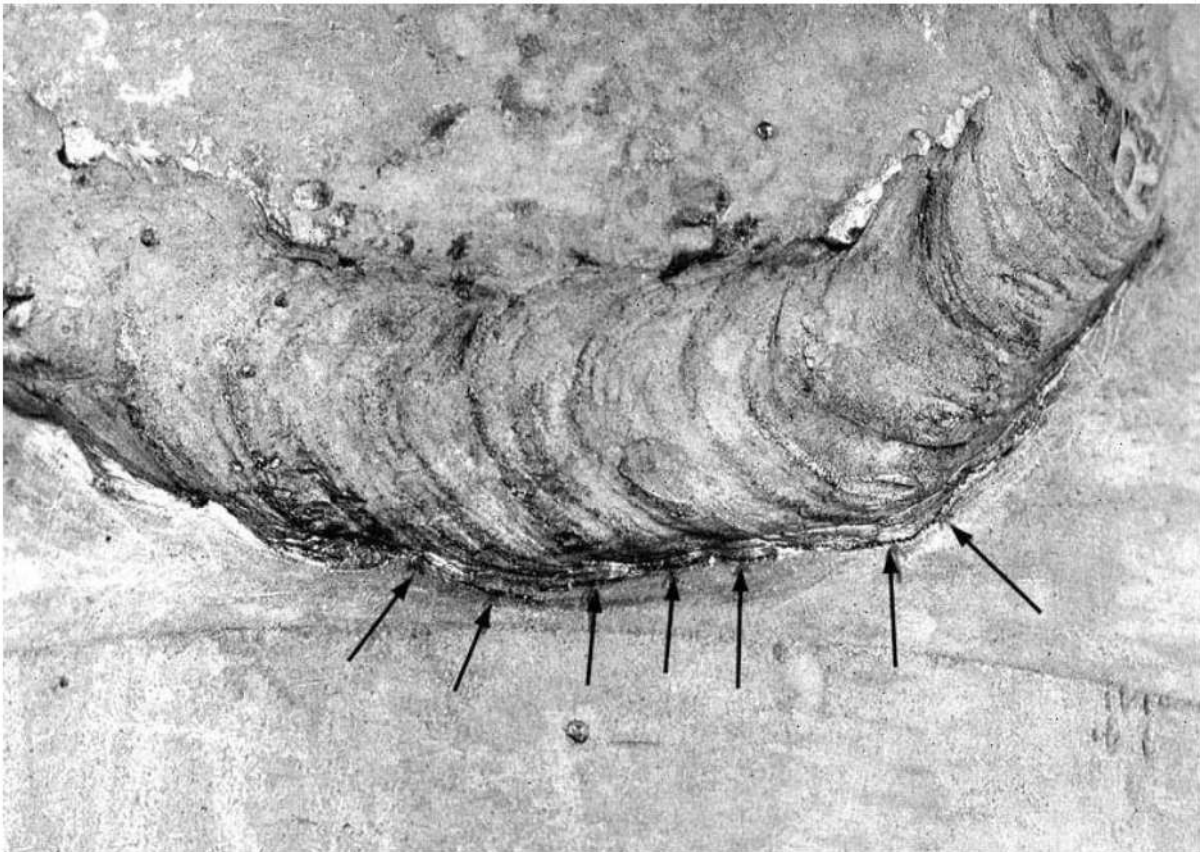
Aspecto de otra parte soldada, en la cual están marcadas por flechas pequeñas grietas en situación análoga a las representadas en la figura 3.
